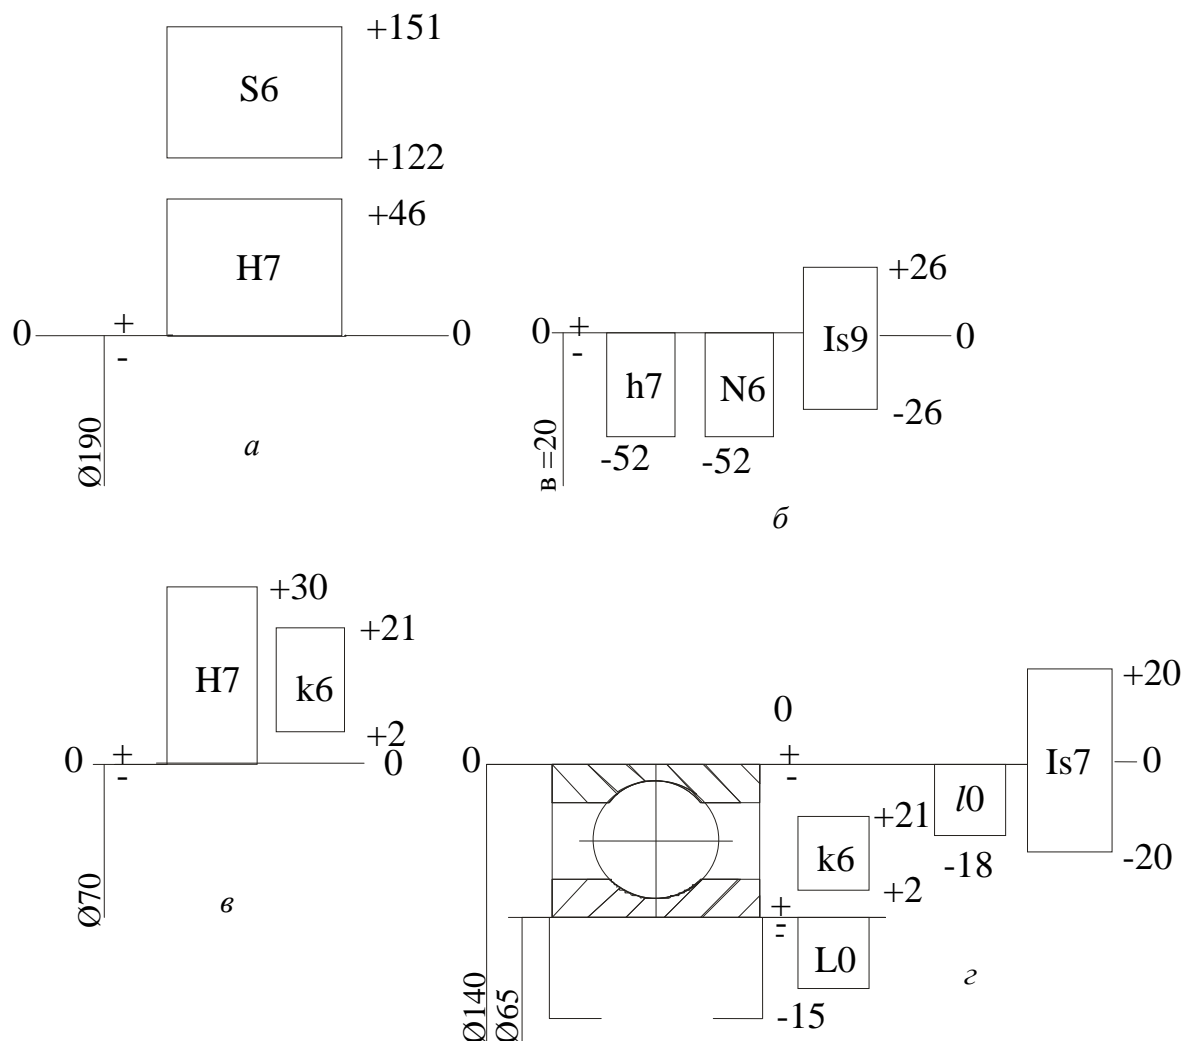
Схемы расположения полей допусков по сопрягаемым поверхностям деталей червячного редуктора:
